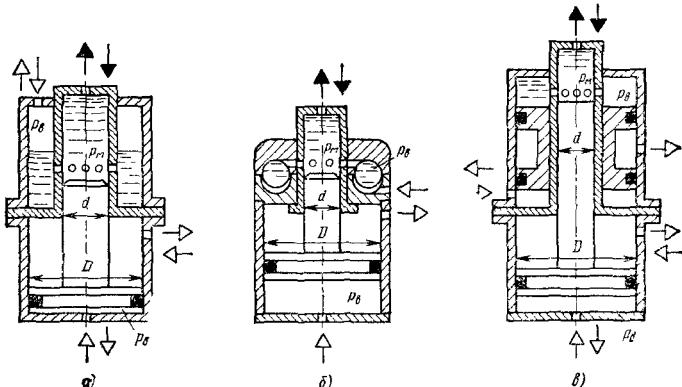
Схемы двухступенчатых пневмогидропреобразователей:
